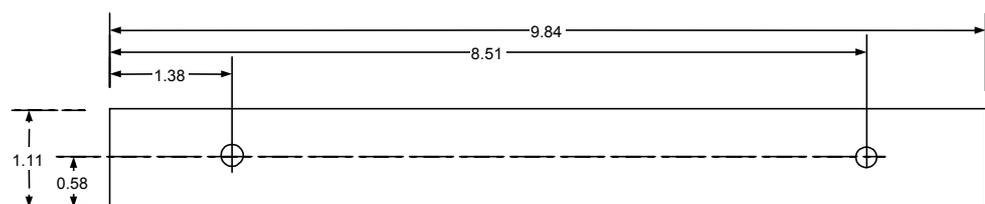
Размеры шины заземления 44В295864-001, вид сзади с монтажными отверстиями
